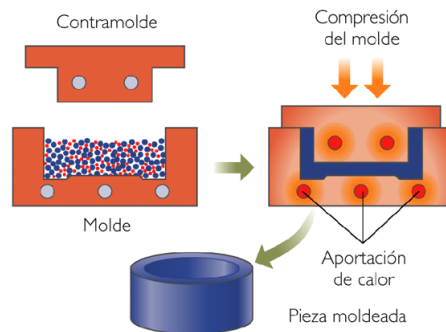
Esquema de un aparato de moldeo por compresión.
